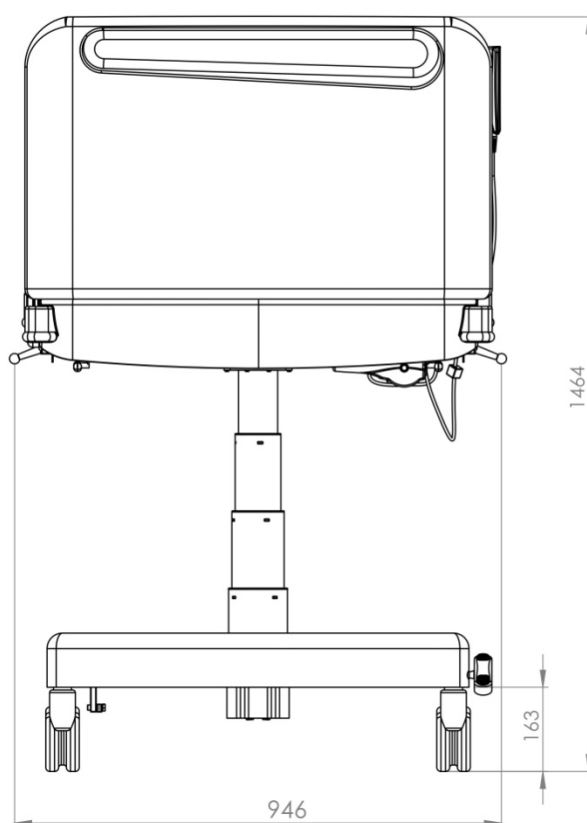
Vista frontal com dimensões gerais para maior altura do lastro. Fonte: Autora.
